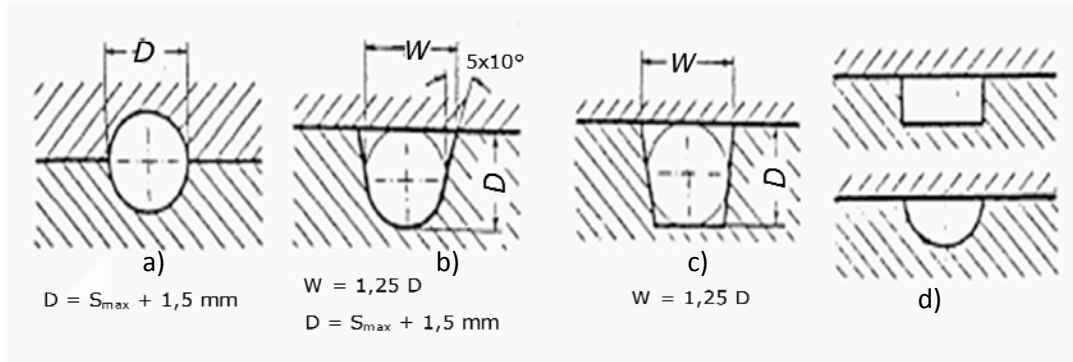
Secțiuni de canale și dimensionarea acestora, [JEA 82]
